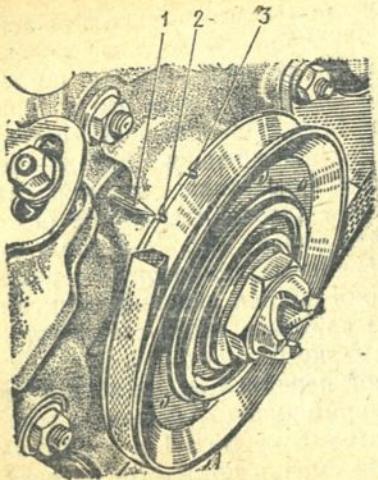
Установочные метки на ободе ведущего шкива коленчатого вала:
